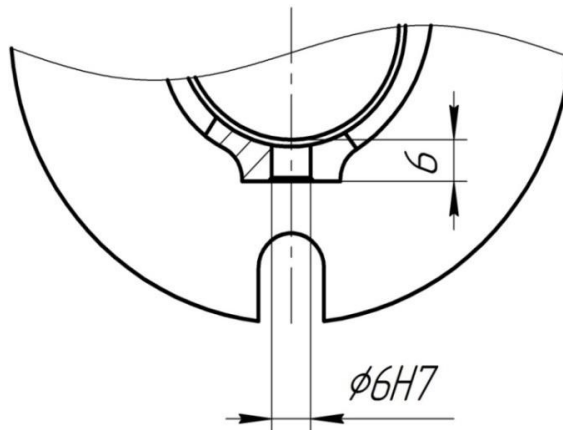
Ескіз оброблюваних поверхонь
